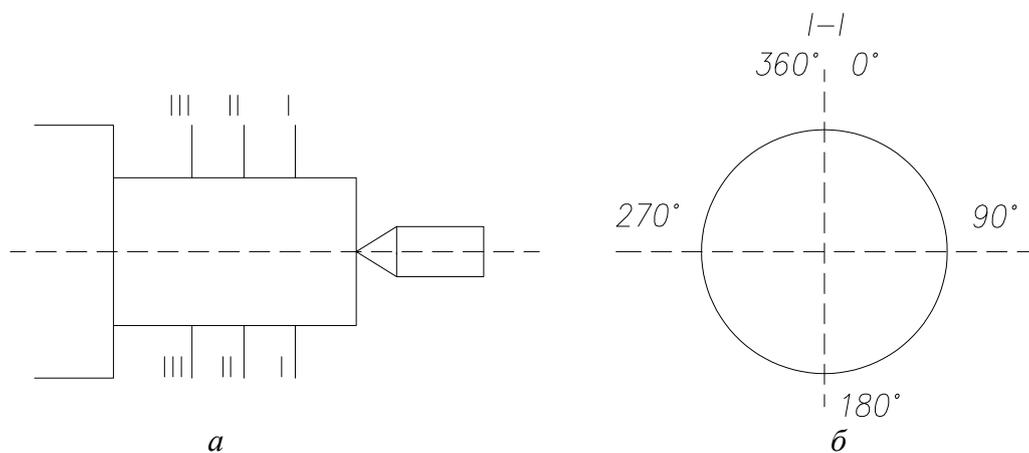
Проверка формы шейки вала: *а* – прямолинейность образующей шейки; *б* – эксцентricность посадочной поверхности
